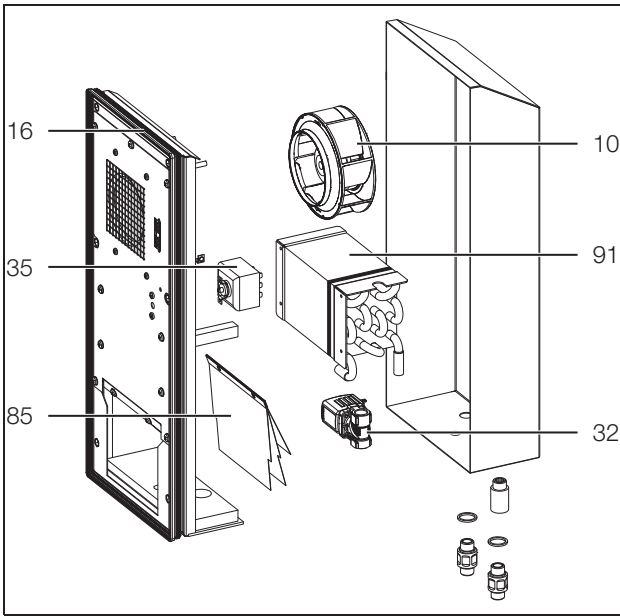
Pièces de rechange 3214.700, 3215.700
